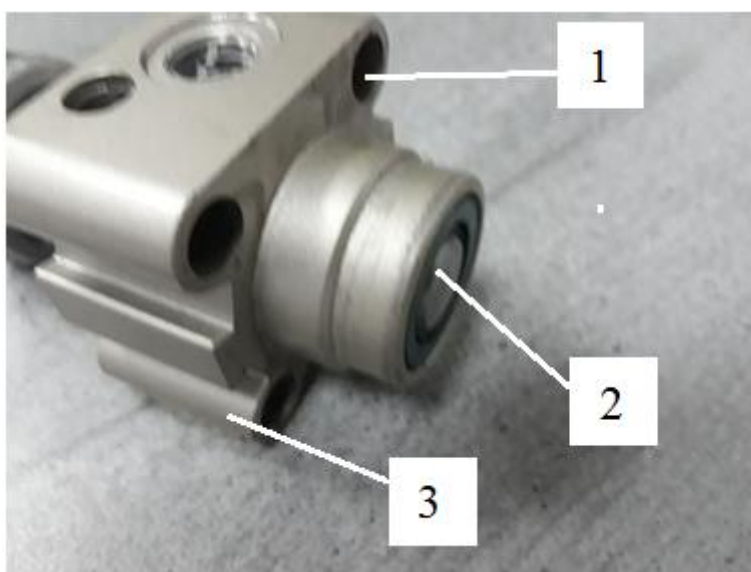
Загальний вигляд передньої кришки пневмомолота.
